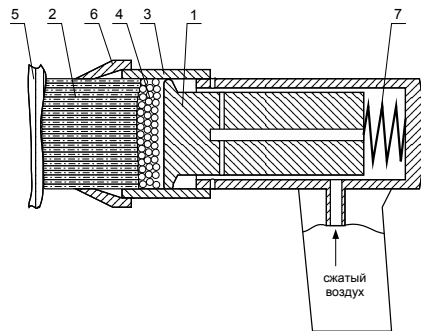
Схема многоконтактного виброударного инструмента ШСУ:
